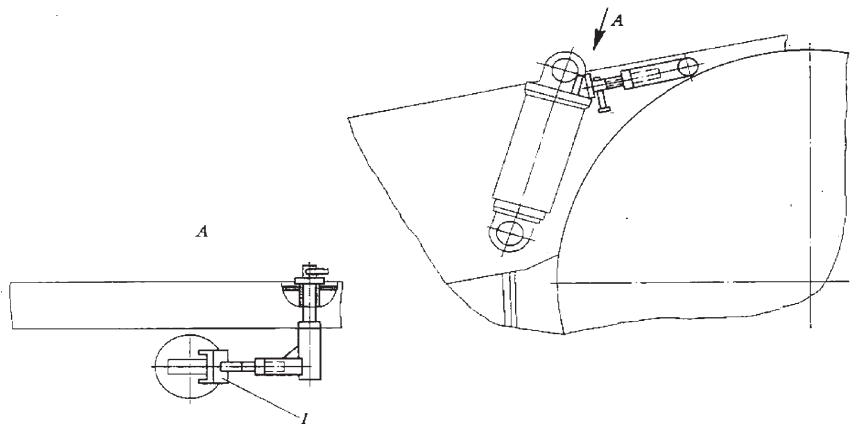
Схема установки приспособления для фиксации цилиндров опрокидывающего механизма при соединении верхних головок цилиндров с кронштейнами платформы; 1 – упор
